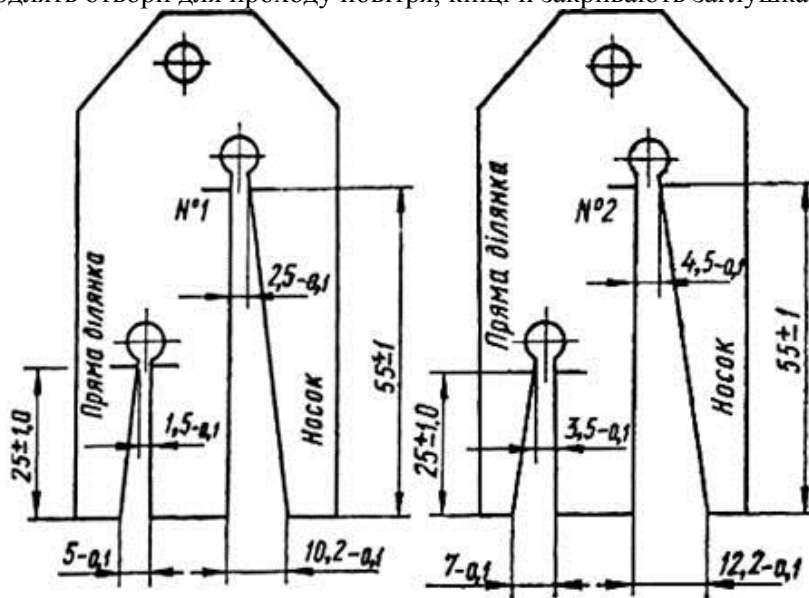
Шабли для контролю форми лека лемеша: а - відтягнутого; б - наплавленого.
